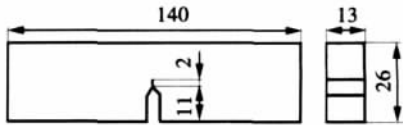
Q420 结构钢 CTOD 试样尺寸 (mm)
